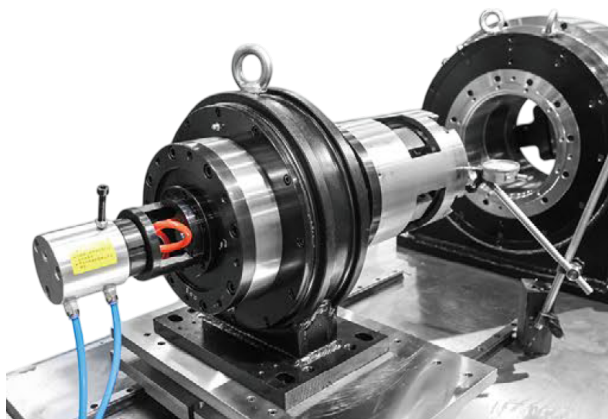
Контроль боковой базовой поверхности заднего патрона.
